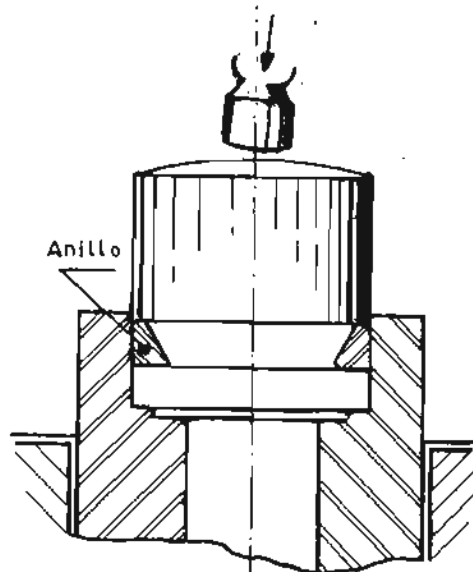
En la morsa con ayuda del cilindro torneado, forzando el anillo externo (montaje en caja).
